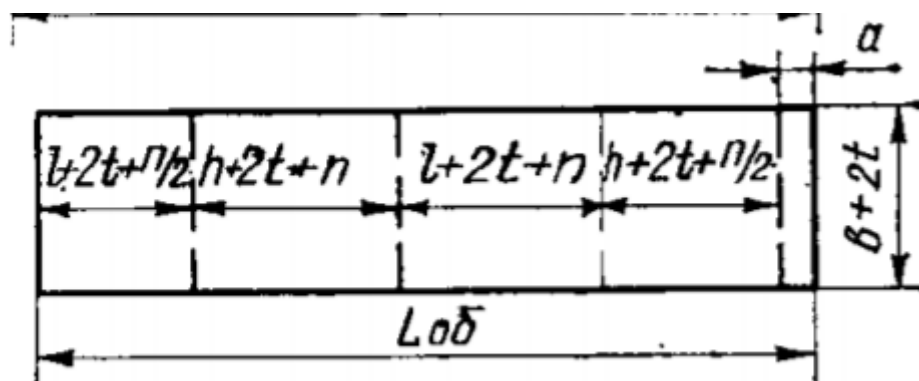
Раскройные карты заготовки ящика и комплектующих изделий (обечайка)
